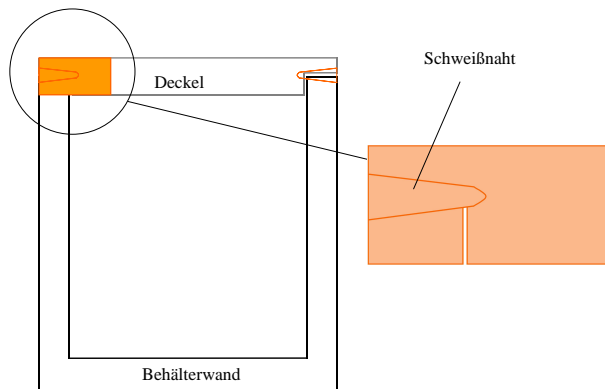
Lage des ringförmigen Spalts senkrecht zur Schweißnaht
